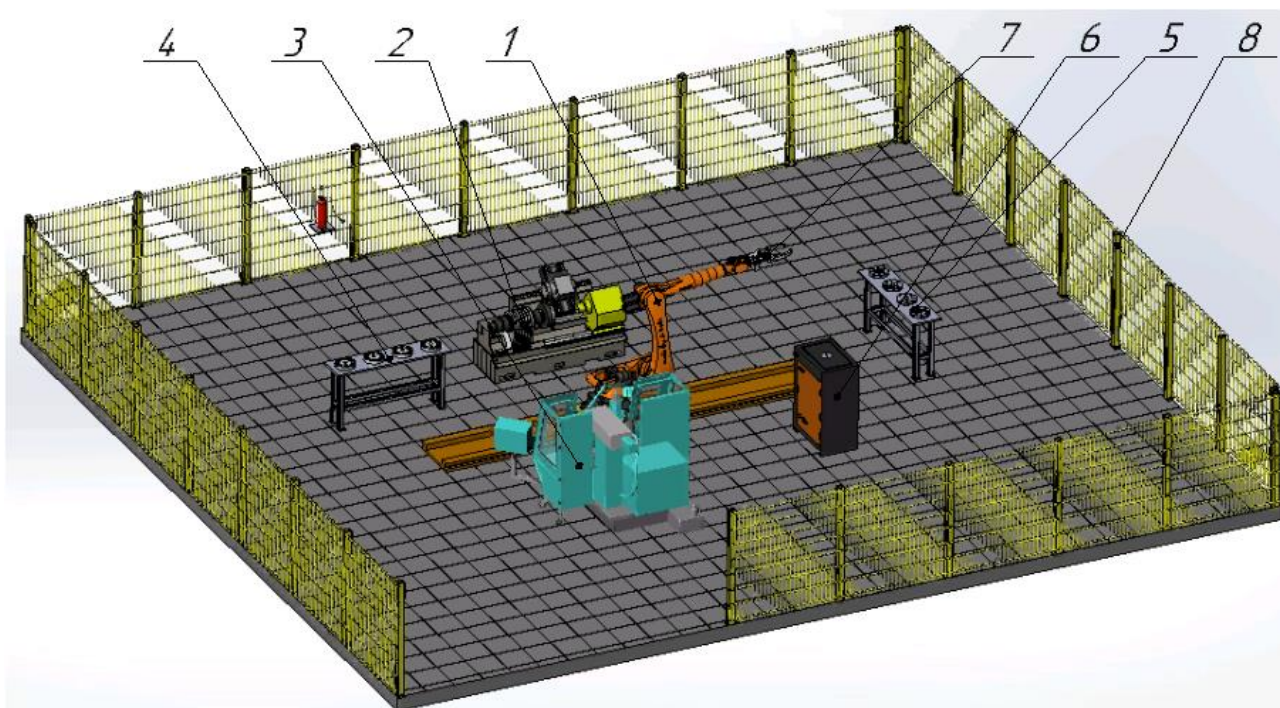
Компоновка РТК для обработки детали «Планшайба»
